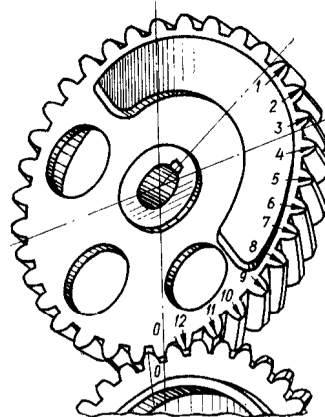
Установочные метки *O* на шестернях балансирующего механизма
